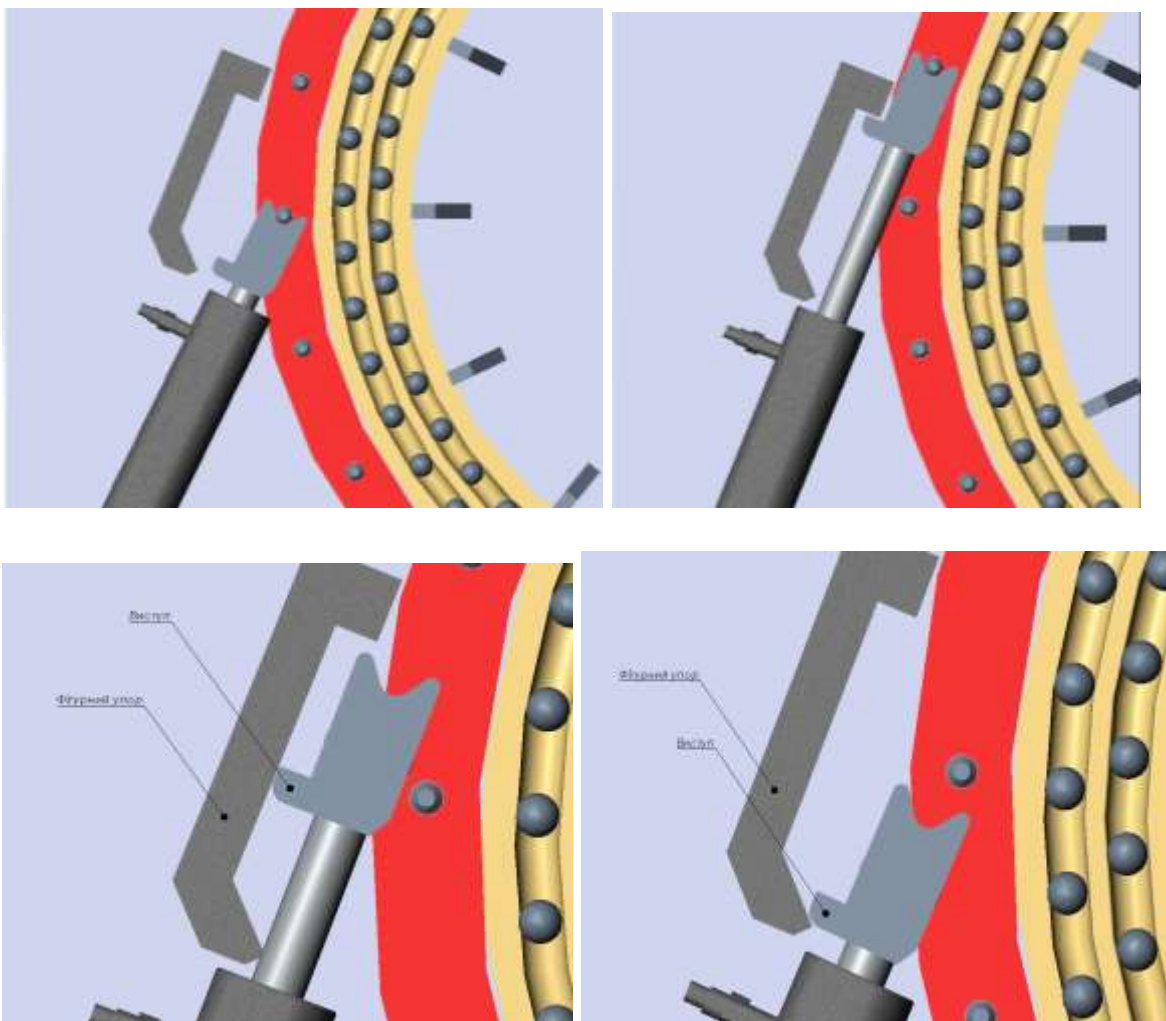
3.7 – Робота поворотного механізму
